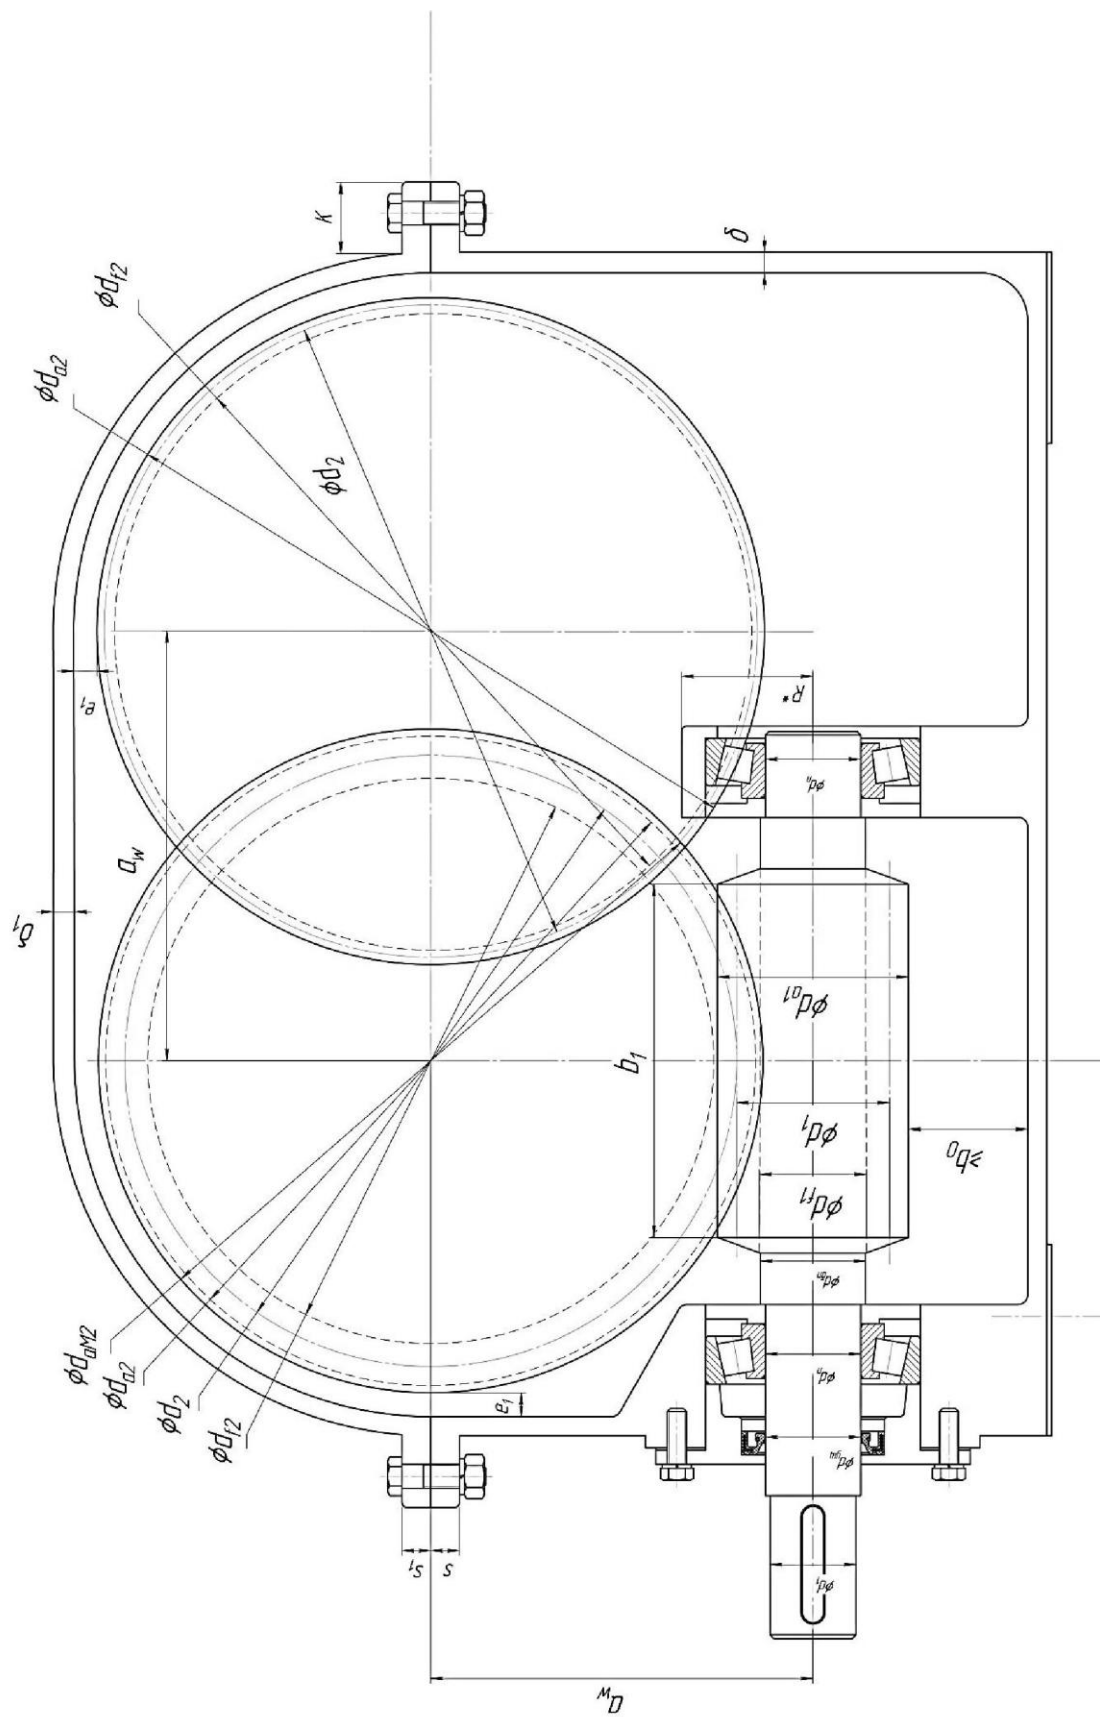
Компонувальне креслення черв'ячно-циліндричного редуктора (початок)
